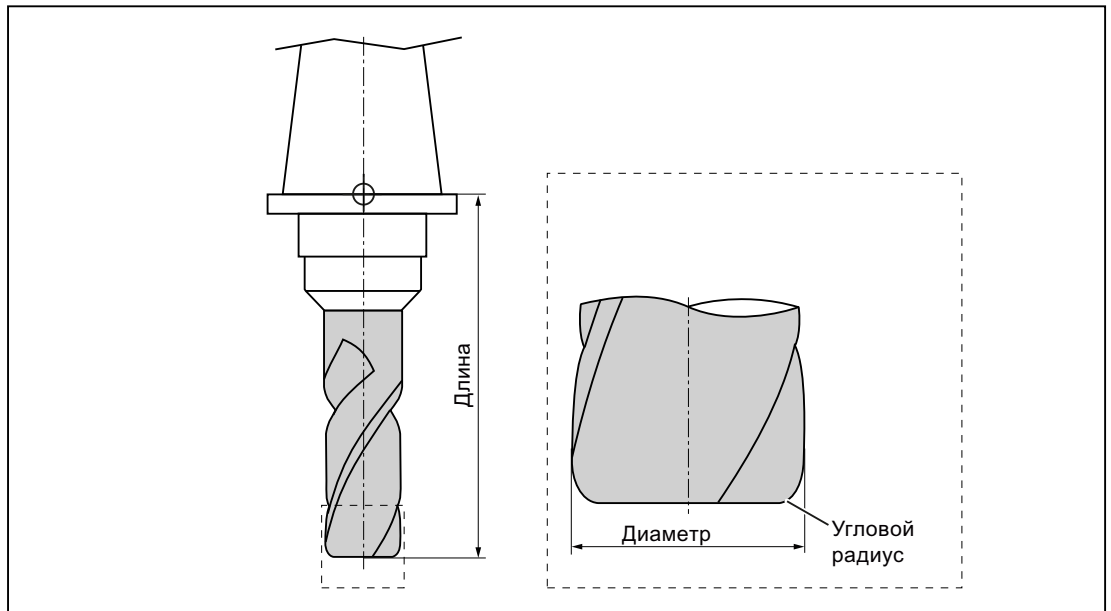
Инструмент 3D на примере концевой фрезы с закруглением углов (тип 121)
